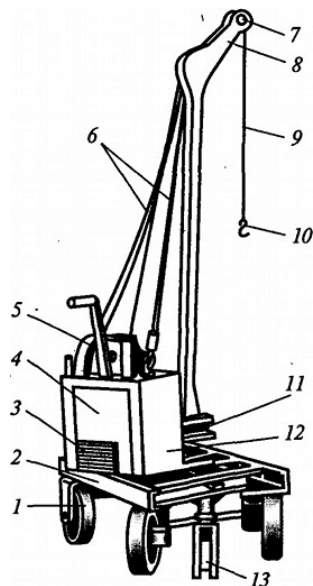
Передвижной поворотный кран: 1 - задние колеса; 2 - тележка; 3 - фиксатор; 4 - противовес; 5 - ручная лебедка; 6 - тяги; 7 - блоки; 8 - стрела; 9 - трос; 10 - крюк; 11 - поворотная рама; 12 - опора; 13 - дышло
